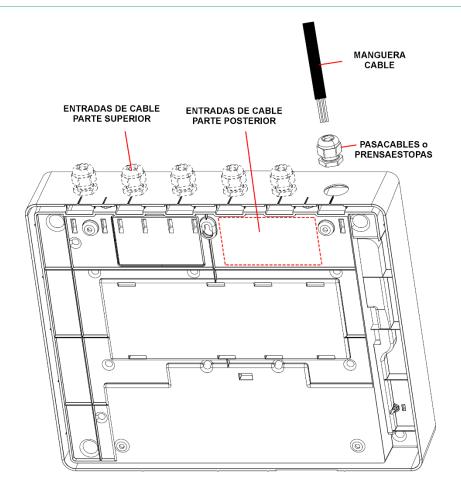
Zonas previstas para entrada de cable en parte trasera.
